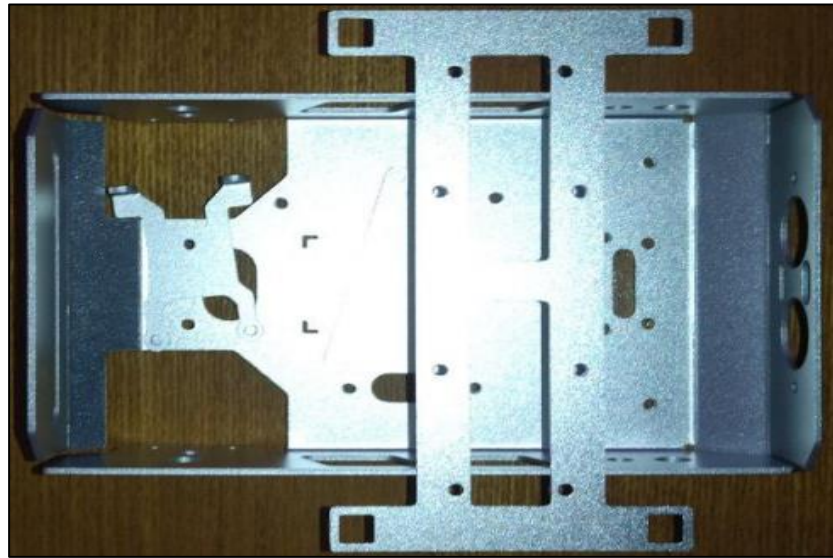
Прямокутний металевий корпус з допоміжними кріпленнями
